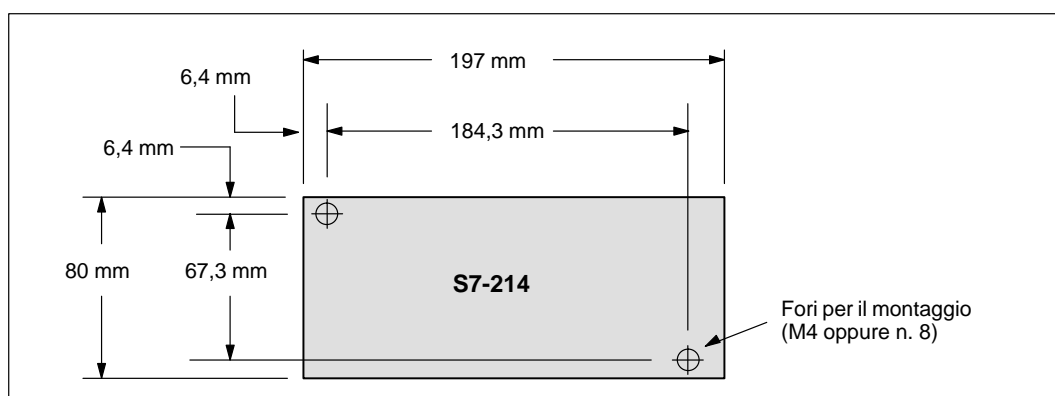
Dimensioni per il montaggio di una CPU S7-214
